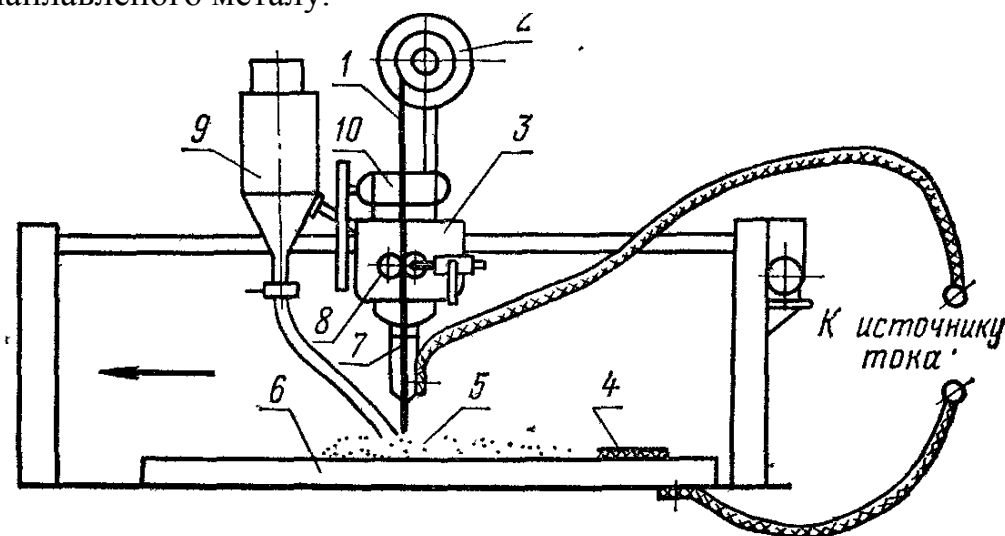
Схема автоматичного зварювання (наплавлення) під шаром флюсу: 1 — електродний дріт, 2 — касета з дротом, 3 — механізм подачі, 4 – жувільна кірка, 5 – шар флюсу, 6 – деталь, 7 – наконечник, 8 – ролики для протягування механізму подачі, 9 – бункер із флюсом, 10 – електродвигун
